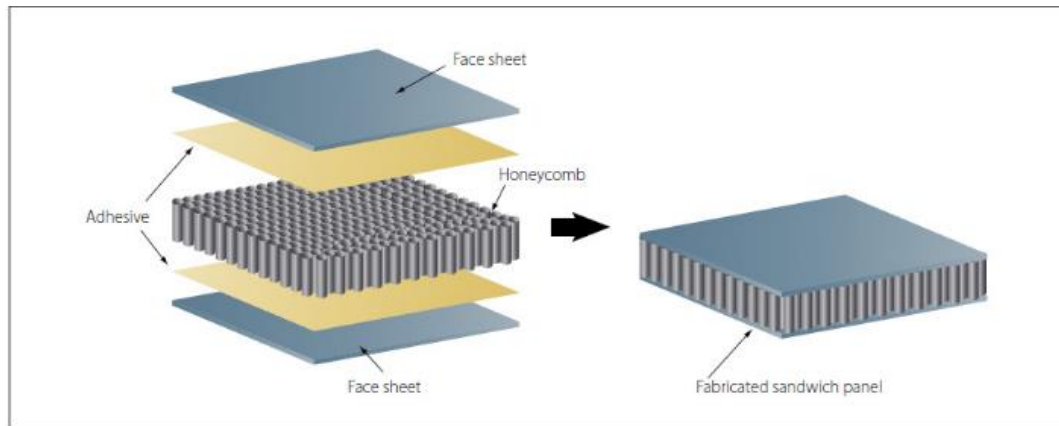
Esquema de estructura tipo sándwich con núcleo de colmena ^[10]
